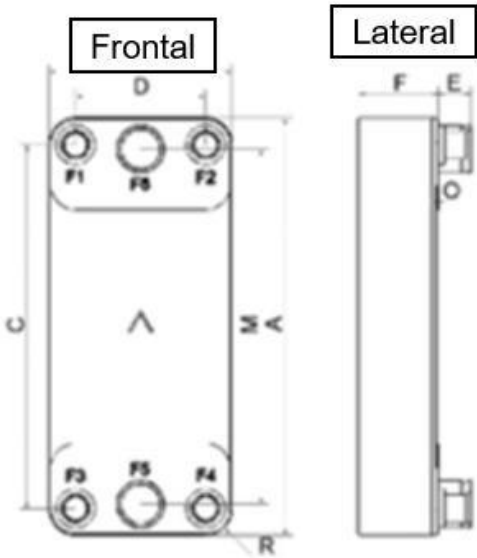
Desenho técnico do trocador de placas. Fonte: SWEP (2023).
